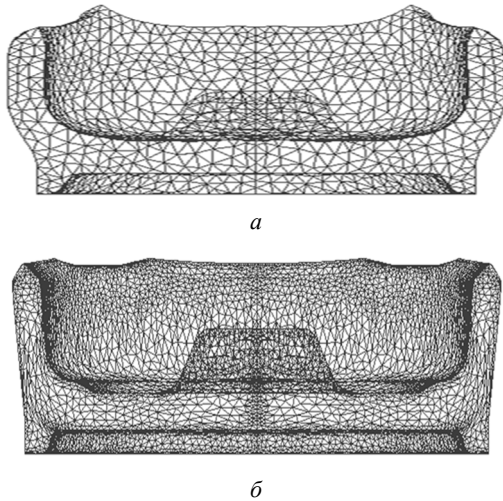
Форма торця стінки половини напівфабрикатів після видавлювання заготовок квадратного перерізу: а – заготовки без фасок, б – заготовки з фасками
